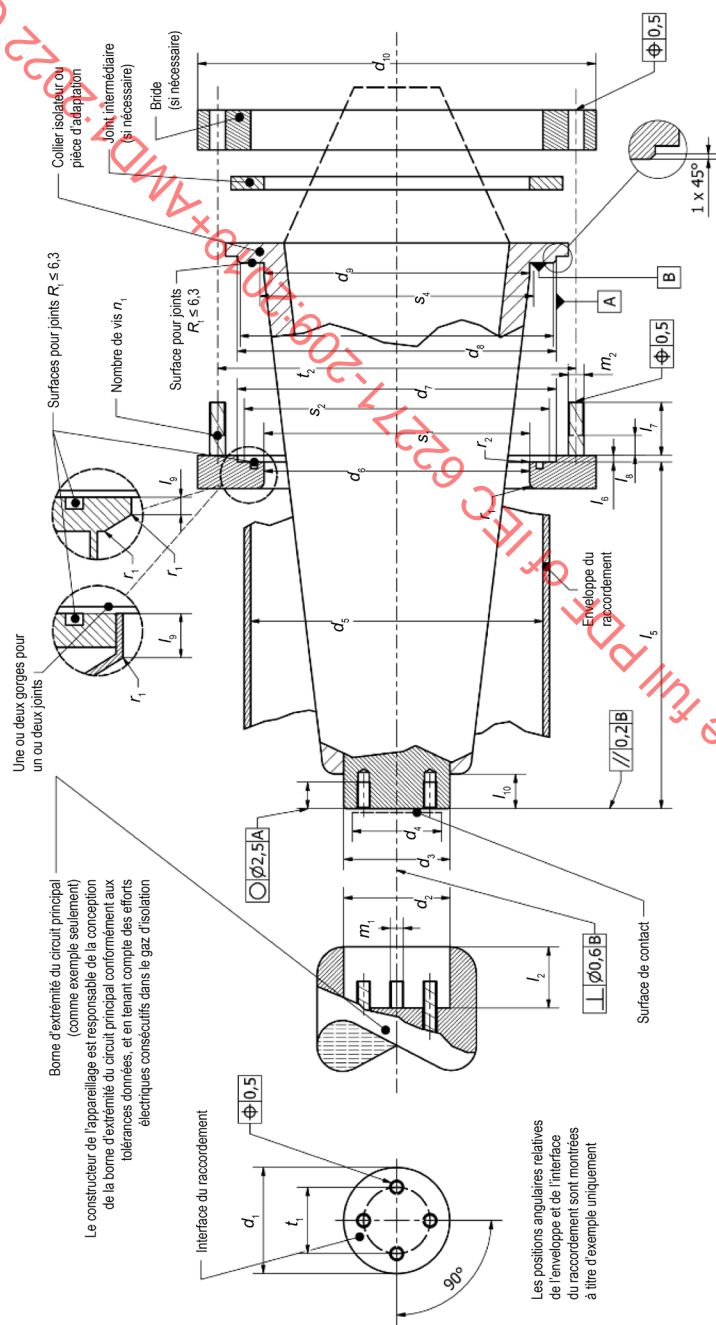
Assemblage de raccordement de câble sec – Exemples de dispositions
